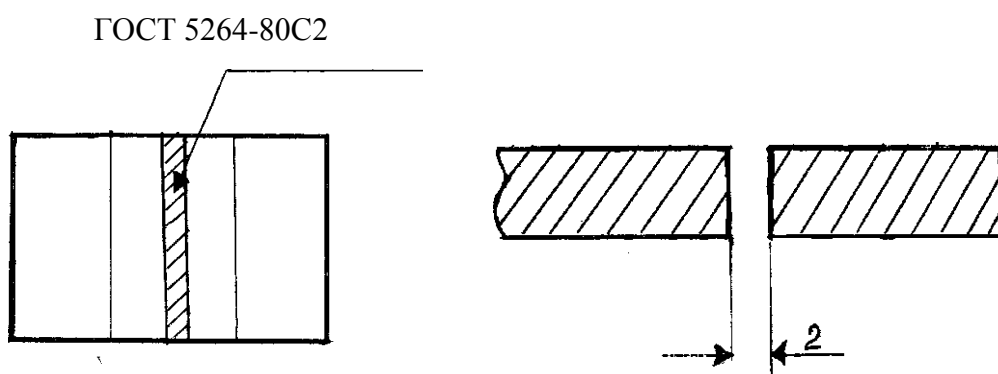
Эскиз сварного соединения пластин встык
